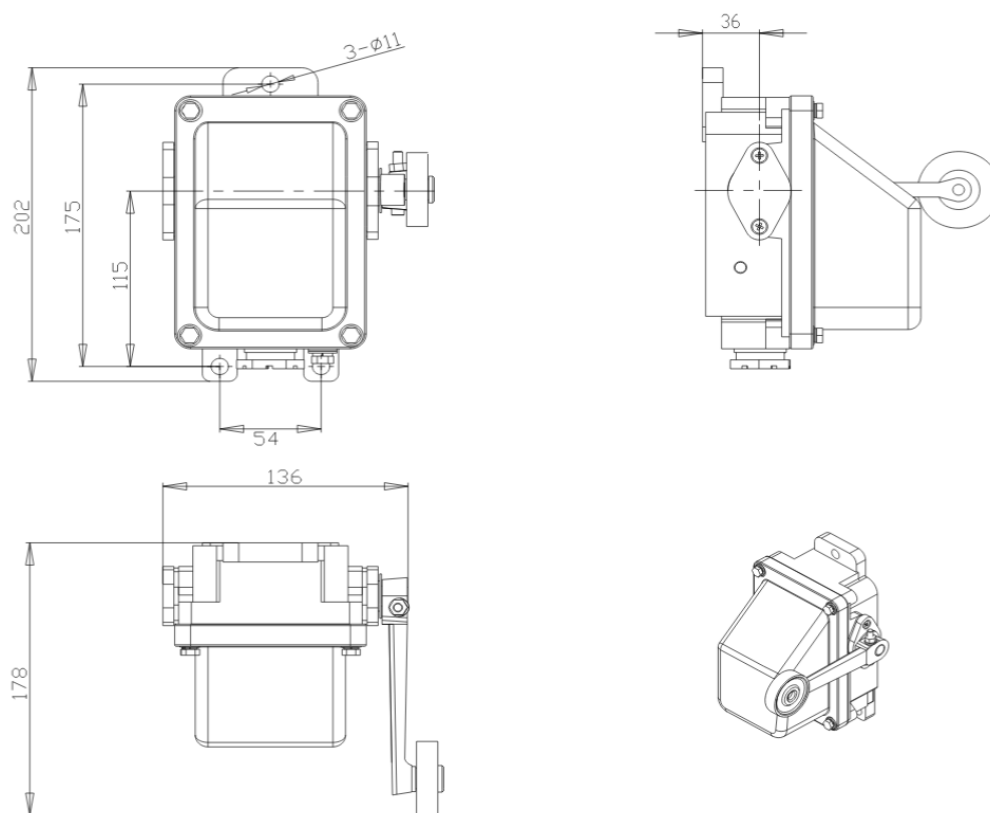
Габаритные размеры концевых выключателей КУ-701
